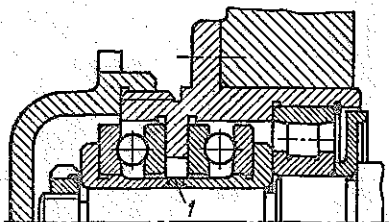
Конструкция фиксирующей опоры с радиальным и упорным подшипниками
